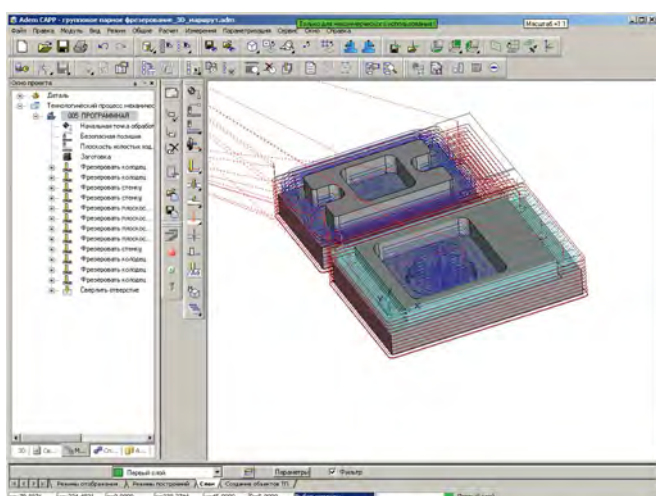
Маршрут и траектории групповой парной обработки с общей заготовкой
